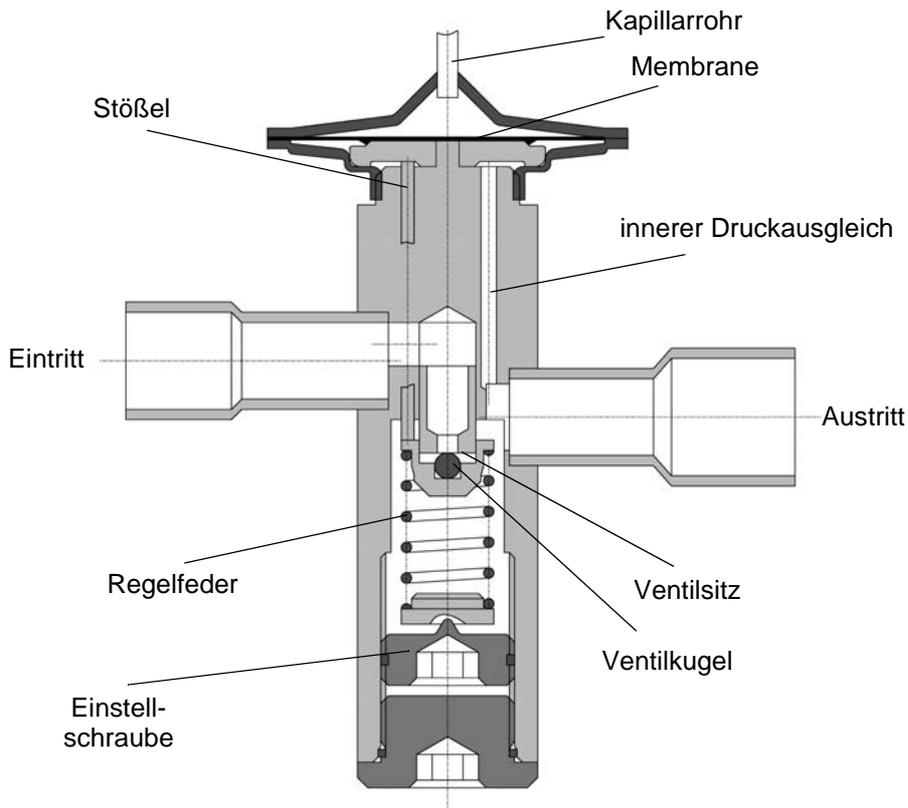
Schema eines thermostatischen Expansionsventils mit innerem Druckausgleich
